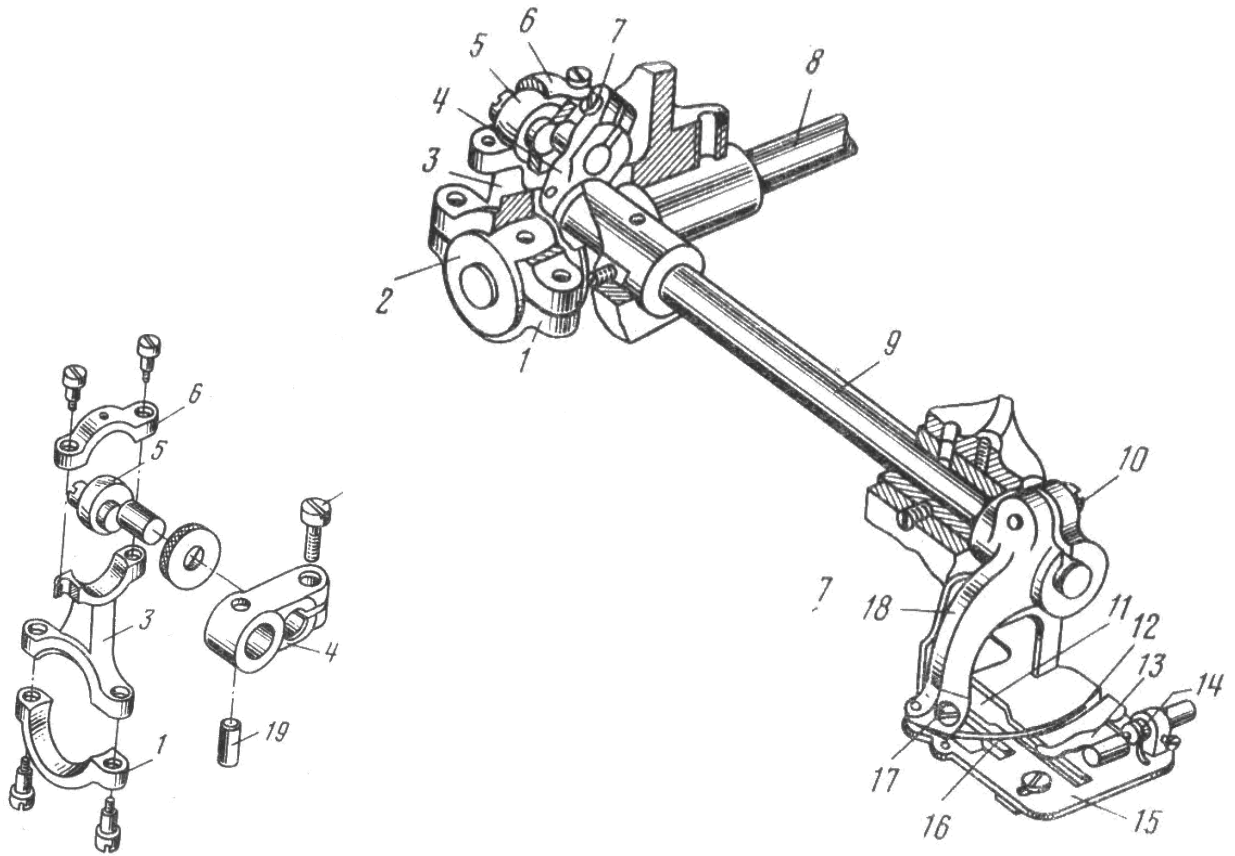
Конструктивна схема механізму голки швейної машини 85 кл. ПМЗ
